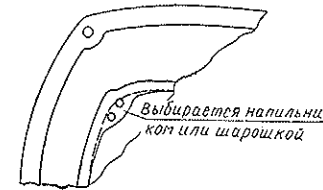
Подготовка картера для установки шестерен модернизированных рычагов переключения передач — № 2 и № 3.
